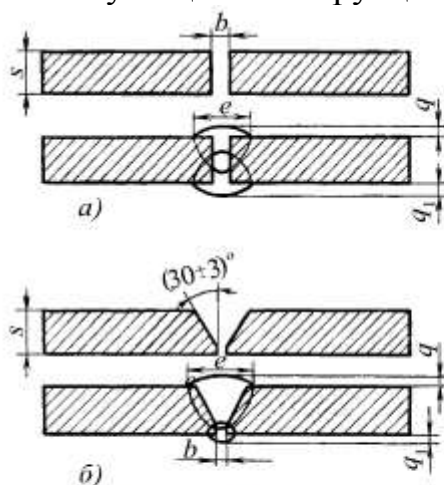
Основные конструктивные элементы сварных швов:
